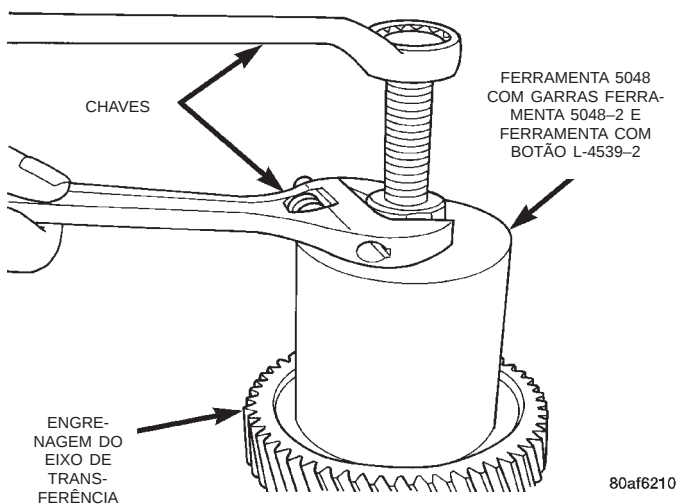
Remoção do Cone do Rolamento da Engrenagem de Transferência
